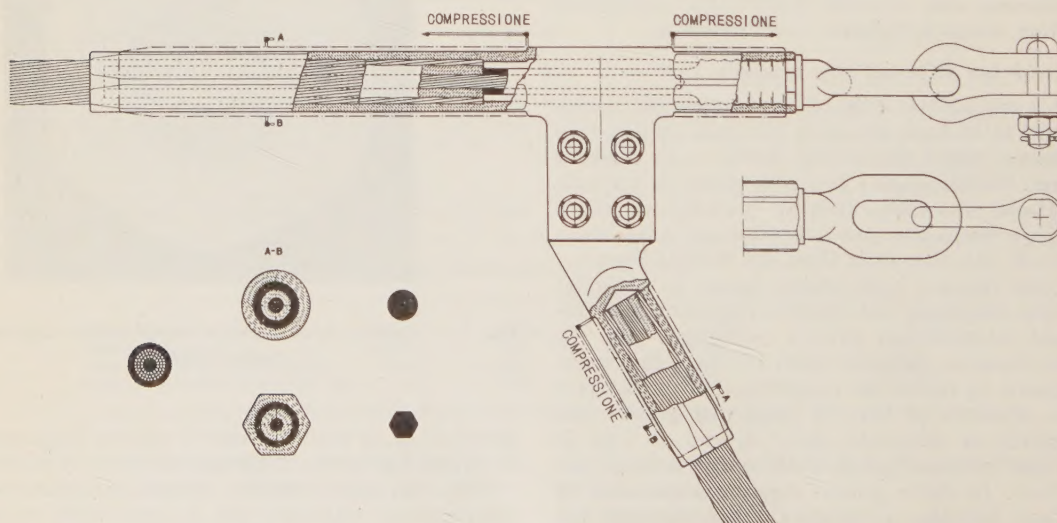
Morsa di ormeggio a compressione per conduttore espanso con riempitivo di Fertene, brevetto Alluminio S.p.A. (costruzione SALVI).
